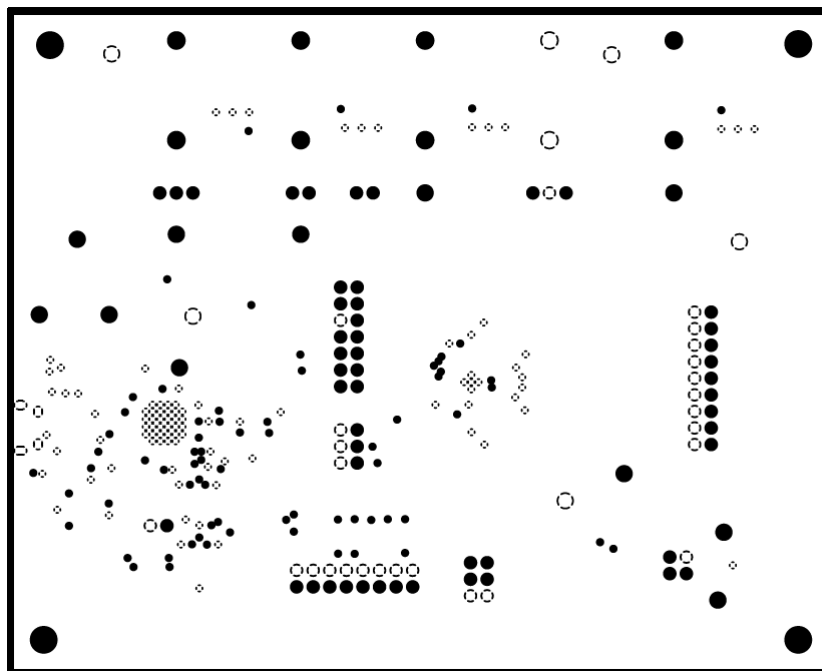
AFE10004EVM PCB 中层 1 布局 (接地平面)
